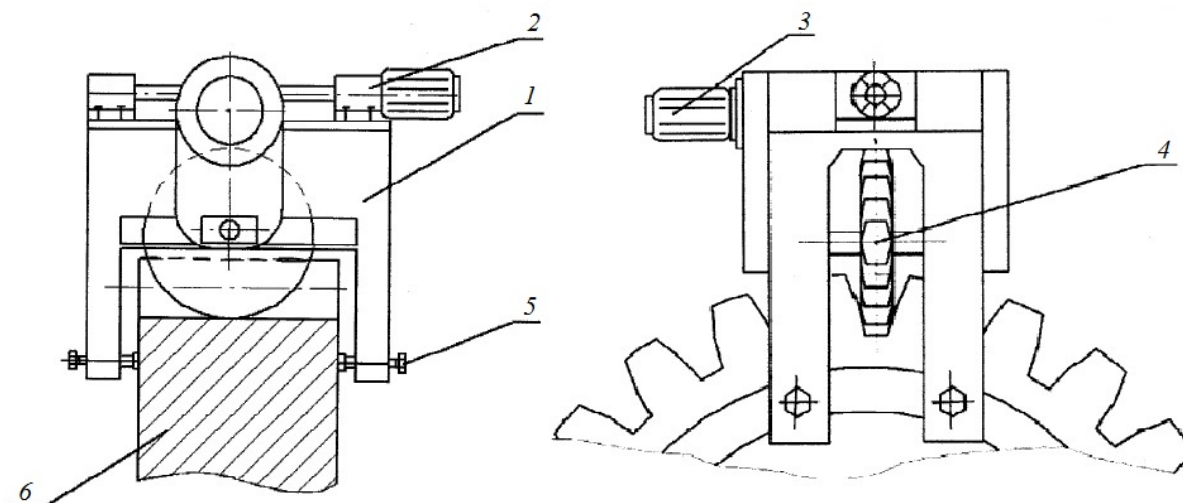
Приставной зубофрезерный станок (Пат. 103505) [13]
